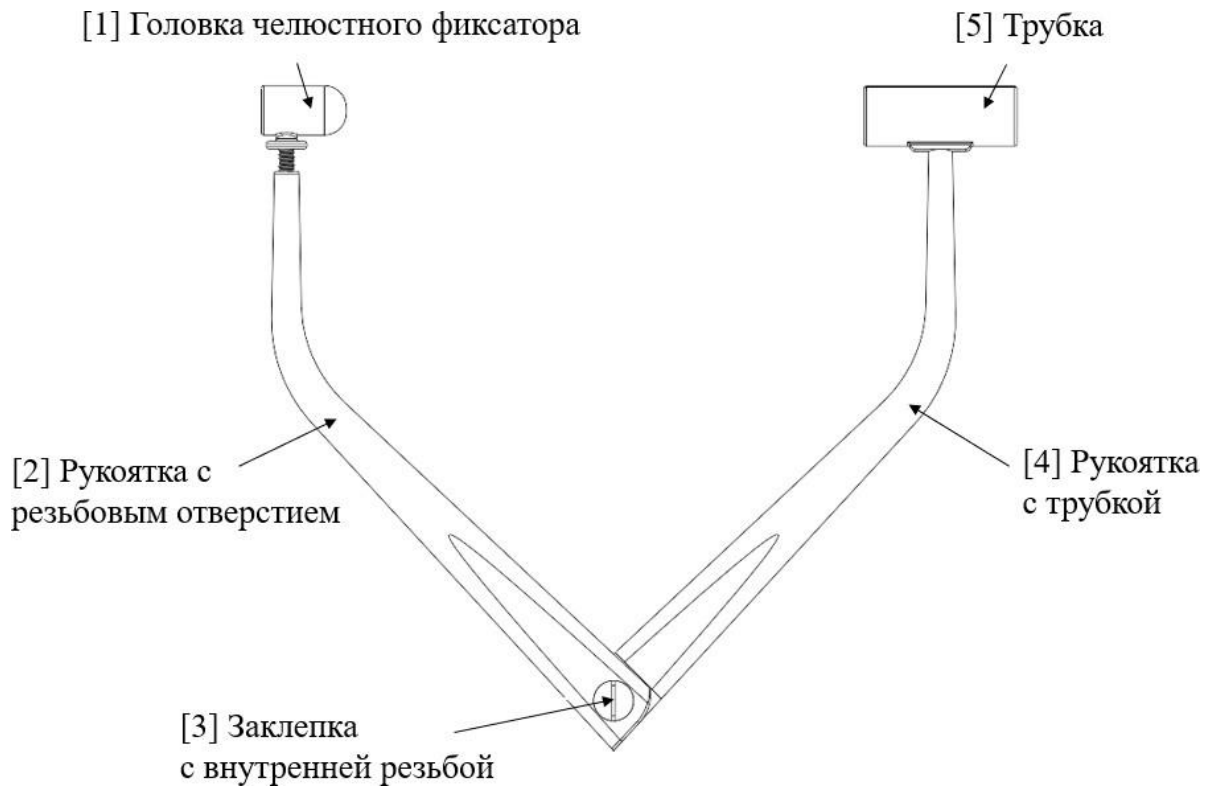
Эскиз навигатора для блокады нижнего альвеолярного нерва
